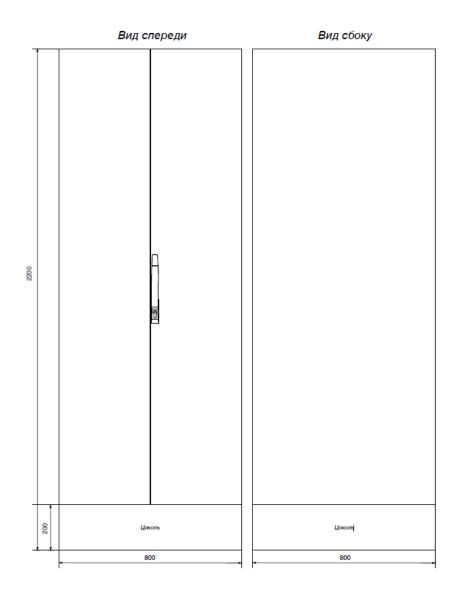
Внешний вид и габаритные размеры концентратора с двухстворчатыми дверями
